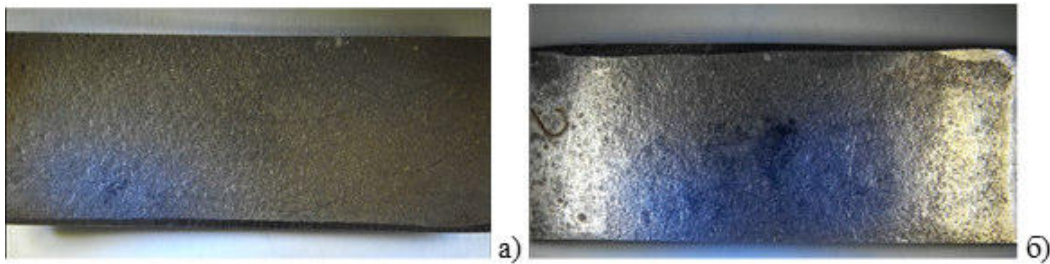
Съемный литой образец – имитатор пера лопатки из стали 08X14H7МЛ: а) вогнутая часть; б) выгнутая часть
